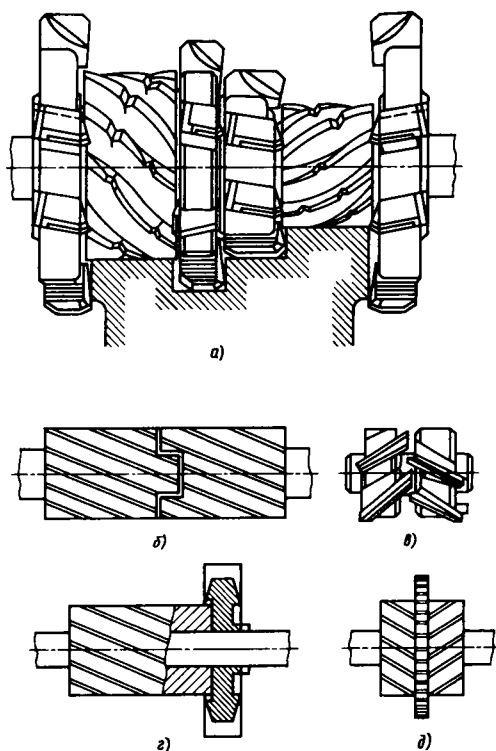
Набор фрез (а) и способы их соединения (б—д)
